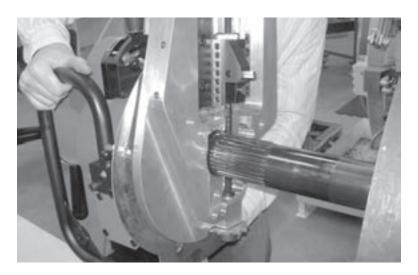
Positionnez la machine EP 424 pour la monter sur le mandrin.
